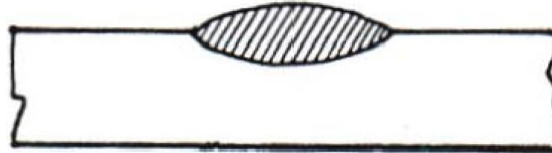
Penetración de la soldadura con electrodo rutílico.
